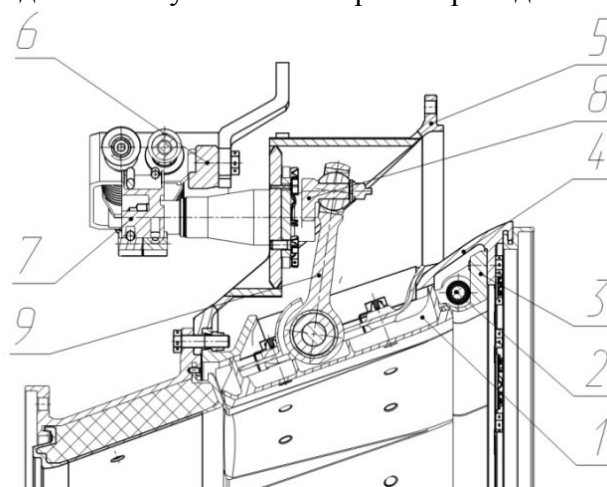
МГР: 1 – створка, 2 – ось, 3 – петля, 4 – корпус внутренний, 5 – корпус наружный, 6 – поводковое кольцо, 7 – шкив, 8 – кривошип, 9 – шатун
